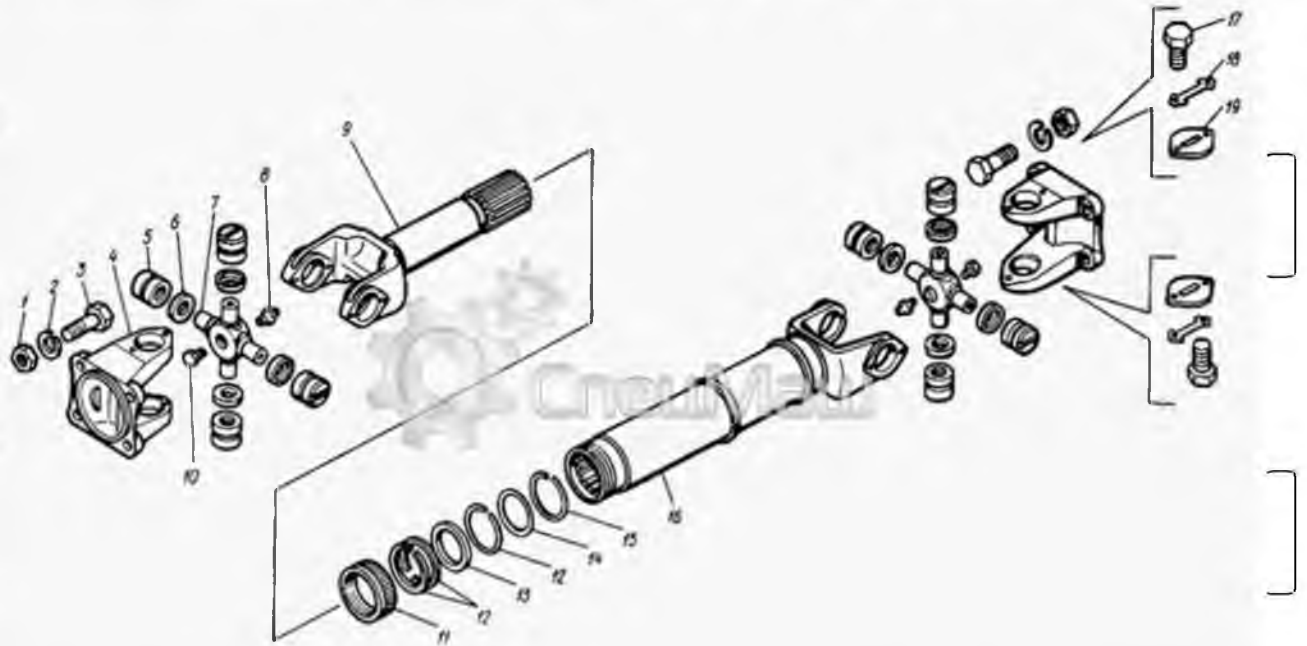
В. Схема установки вала карданного автомобіля КАМАЗ
